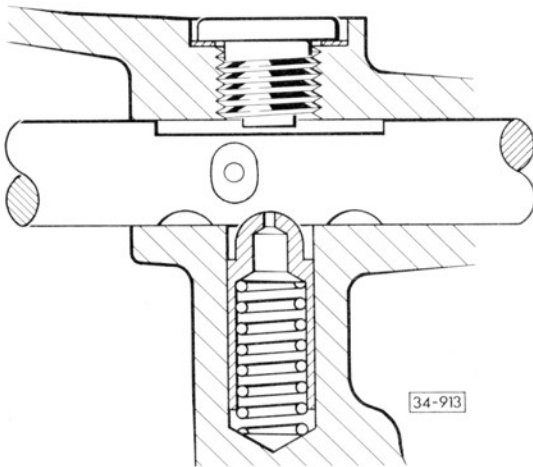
Einbaulage Gangarretierung (1–4 Gang)
